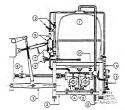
Construcción general de un pulverizador de campo Fuente: Berlijn, 1978
